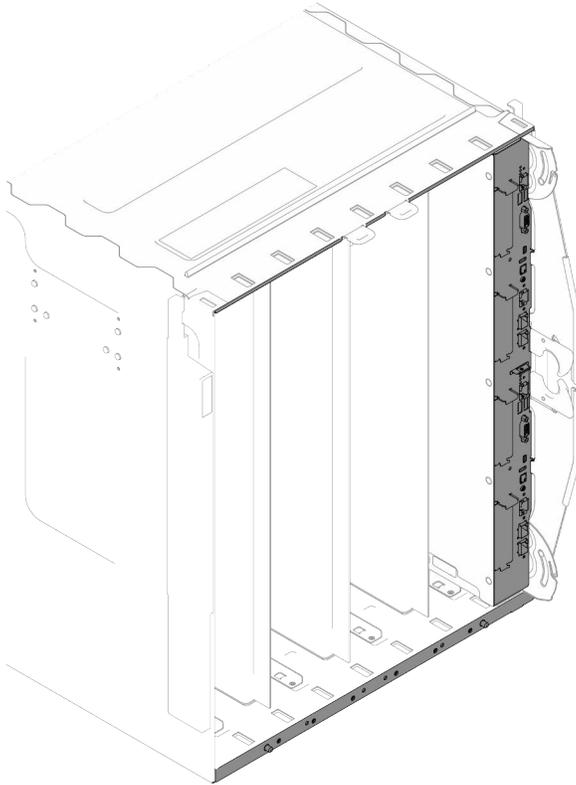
Alignement de la surface du panneau frontal du plateau et du cadre extérieur du boîtier
